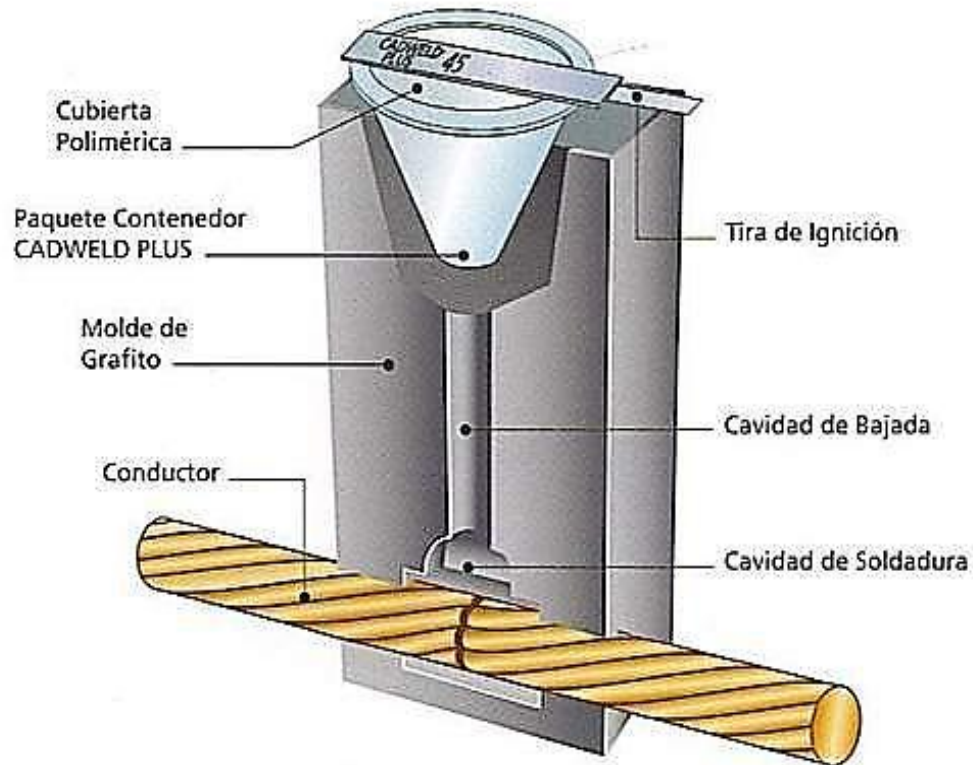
Molde de grafito utilizado para realizar soldaduras exotérmicas
